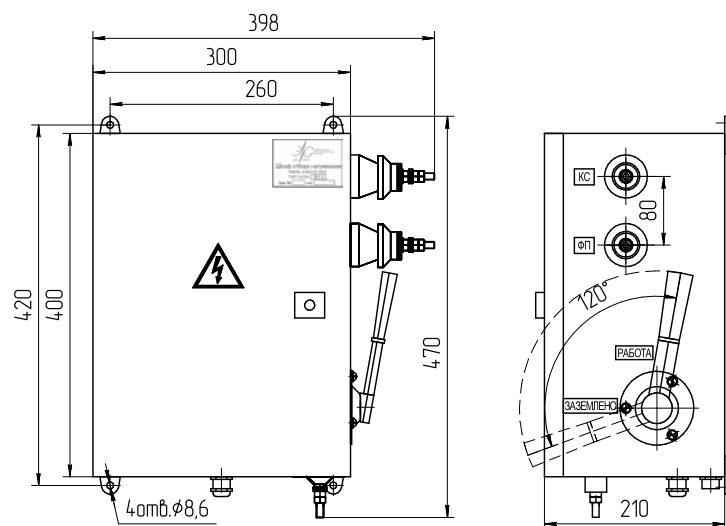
Габаритно-присоединительный чертеж ШОН-301С.
